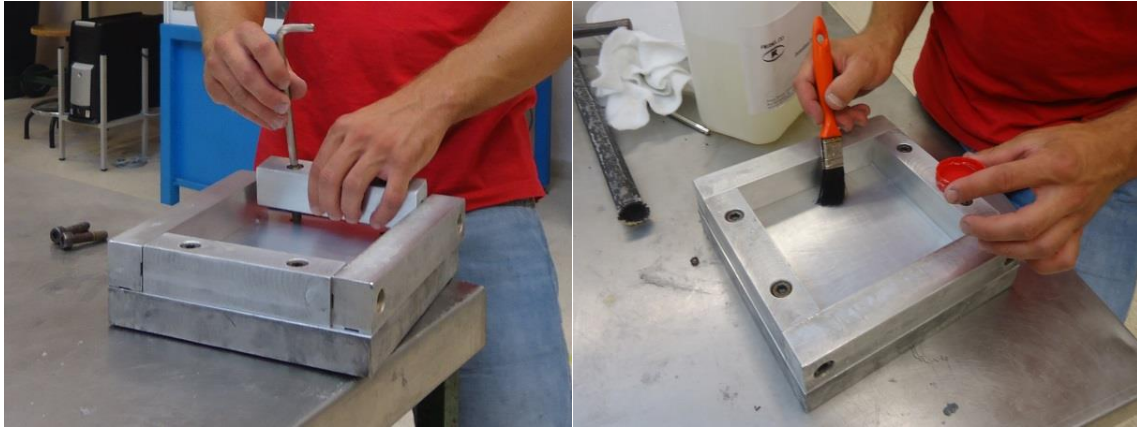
Molde utilizado, montagem e aplicação de desmoldante.
